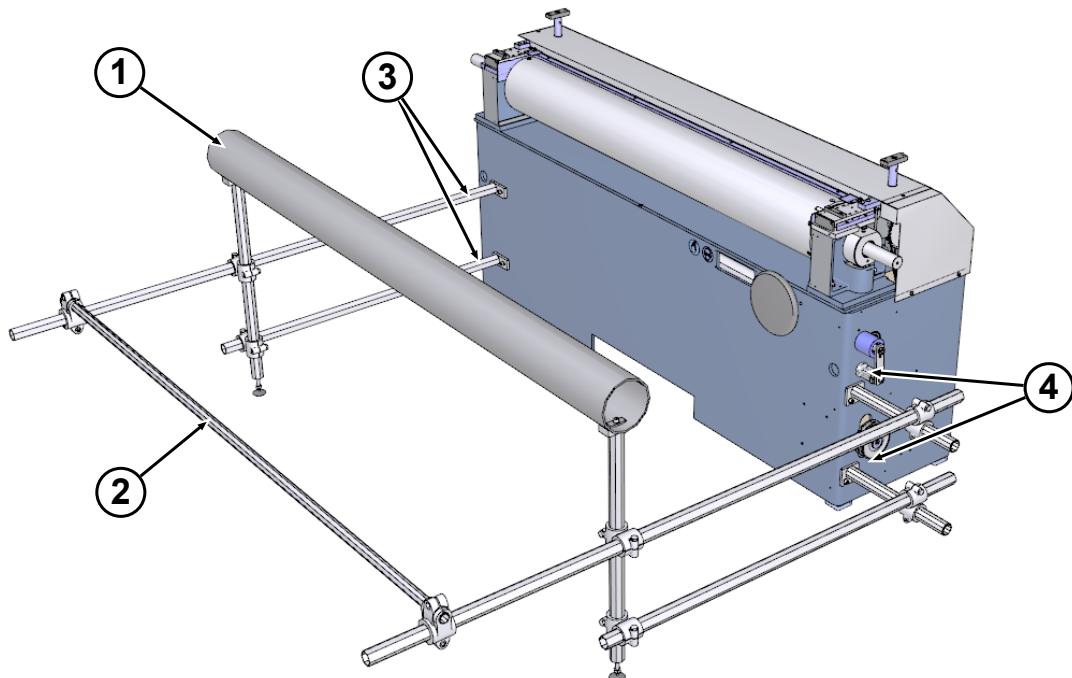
Dispositivo de montaje de la cinta montado en la máquina
